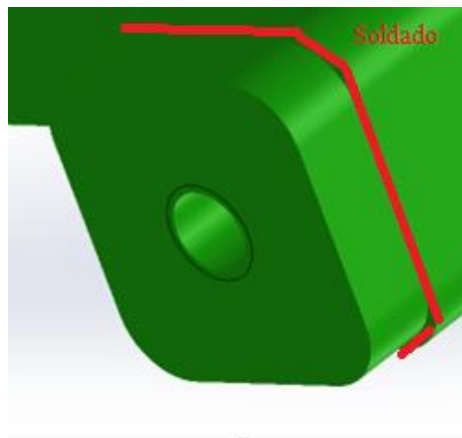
Vista detalla de soldado de pieza N°3 (Fuente 88)
